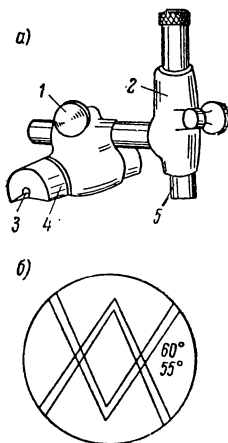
Установка резьбового резца с помощью специальной лупы.
